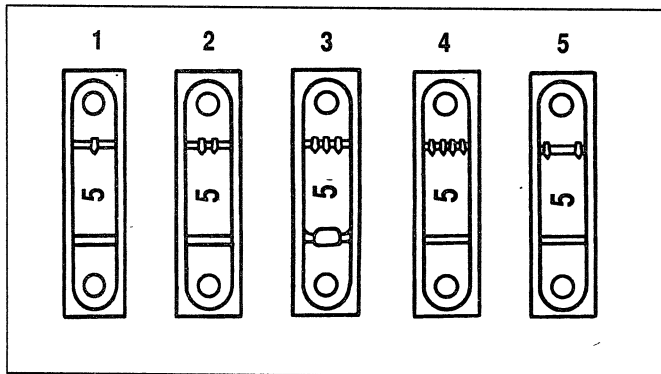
Метки на крышках коренных подшипников (счет опор ведется от передней части двигателя)
